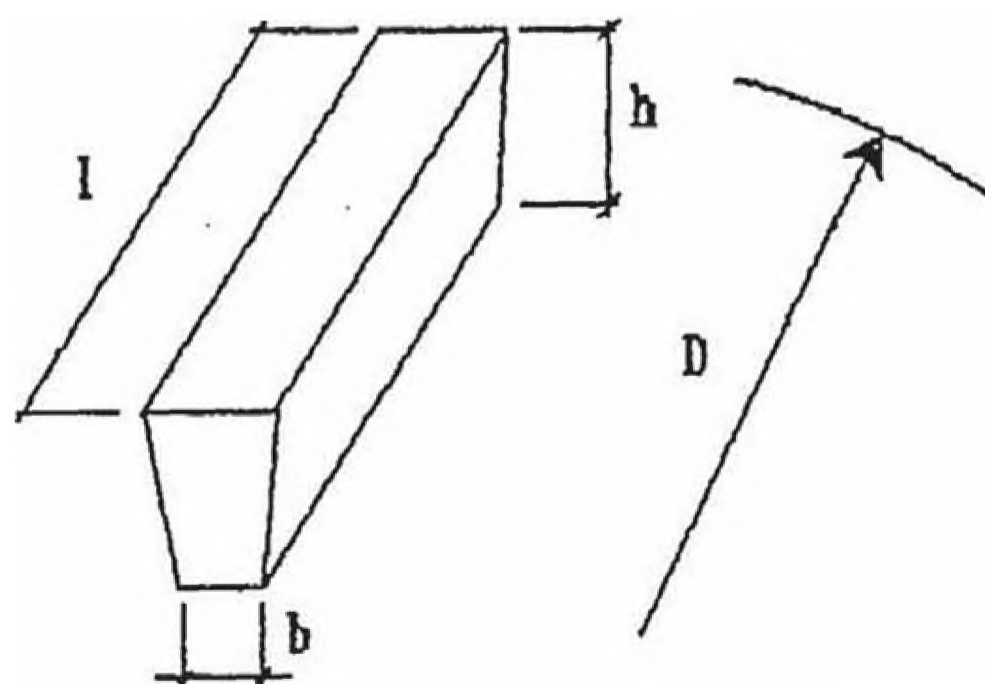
DIMENSIONES DE LADRILLOS PARA HORNOS ROTATIVOS.
